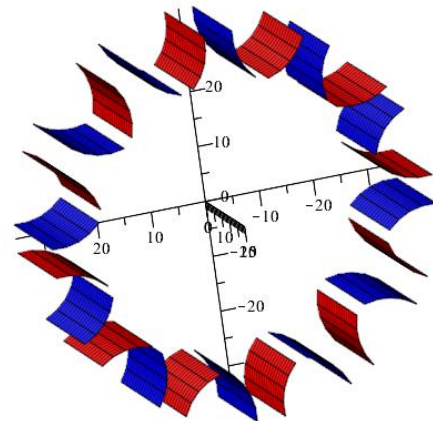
Производящая поверхность, эквивалентная производящей поверхности зуборезного инструмента «долбляк» с модифицированным исходным профилем.
